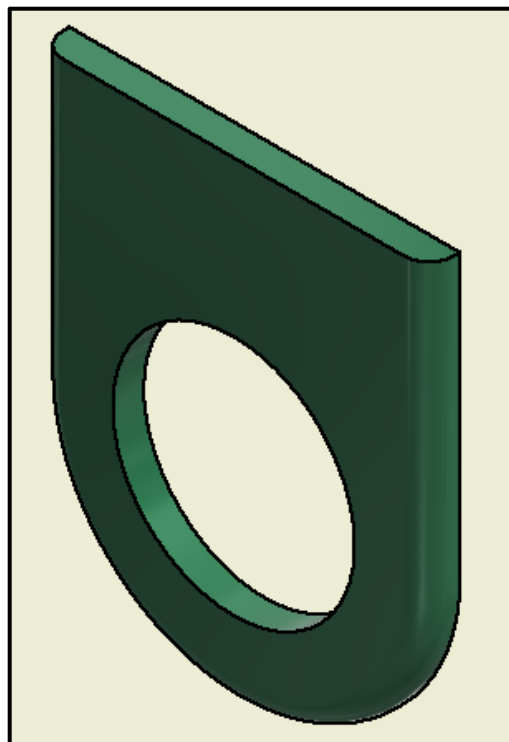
Vista isométrica de la tapa frontal del dispositivo embebido principal
